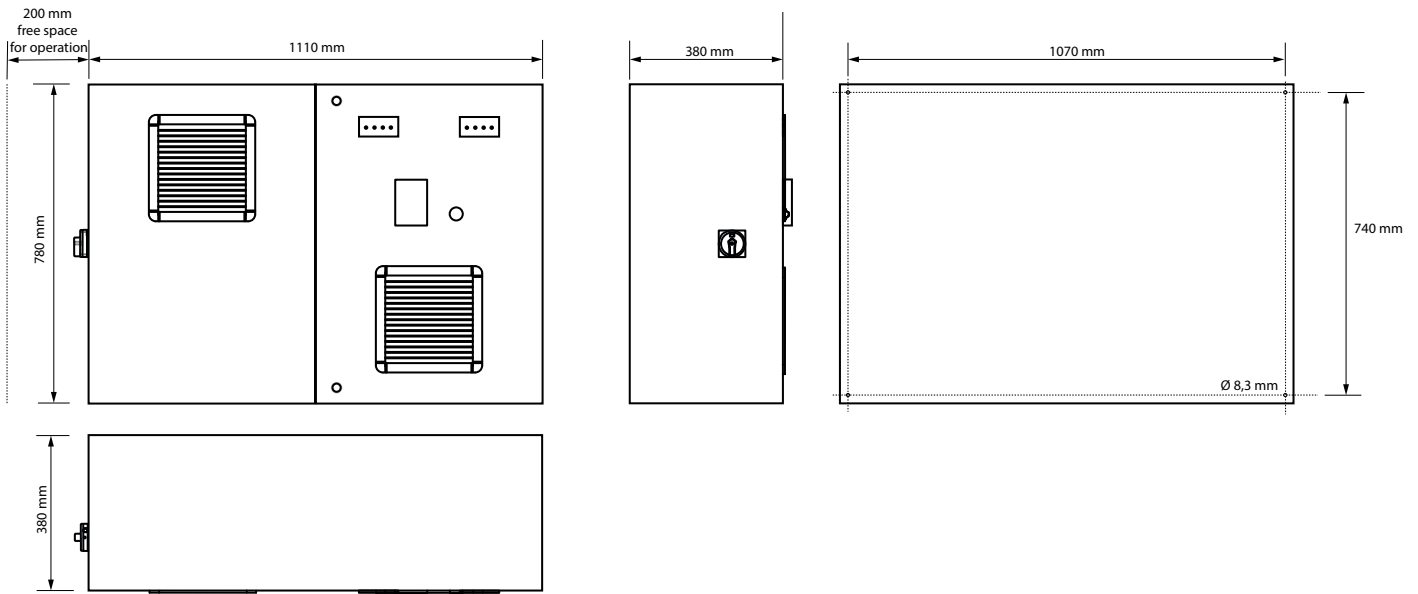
Baugröße BG1110 für direkte Wandmontage (FrigoPack FU+ Kälteumrichter im Steuerschrank)
